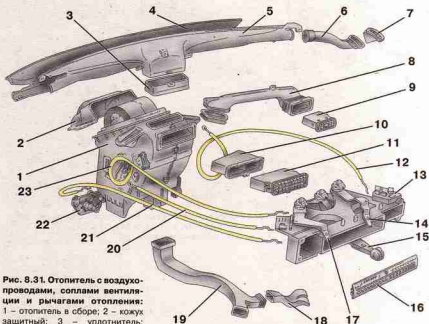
Отопитель с воздуховодами, соплами вентиляции и рычагами отопления: 1 – отопитель в сборе; 2 – кожух защитный; 3 – уплотнитель; 4 – воздуховод передний; 5 – воздуховод задний; 6 – воздуховод правый; 7 – сопло правое; 8 – воздуховод боковой правой; 9 – сопло боковое правое; 10 – корпус промежуточный; 11 – сопло центральное; 12 – тяга заслонки обогрева ветрового стекла; 13 – рычаги управления отопителем; 14 – рукоятка управления заслонкой обогрева ветрового стекла; 15 – рукоятка управления заслонкой обогрева ног; 16 – пластина символов; 17 – рукоятка управления заслонкой обогрева ног; 18 – резистор; 19 – воздуховод обогрева салона; 20 – тяга заслонки управления отопителем; 21 – тяга управления краном отопителя; 22 – кран отопителя; 23 – тяга заслонки обогрева ног
